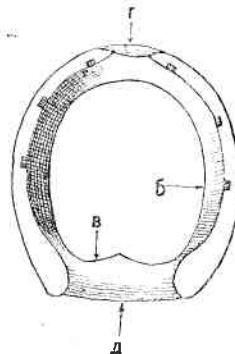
Круглая подкова — верхняя поверхность: а) наружный край, б) бухтовка, в) поперечная ветвь, г) головка.
